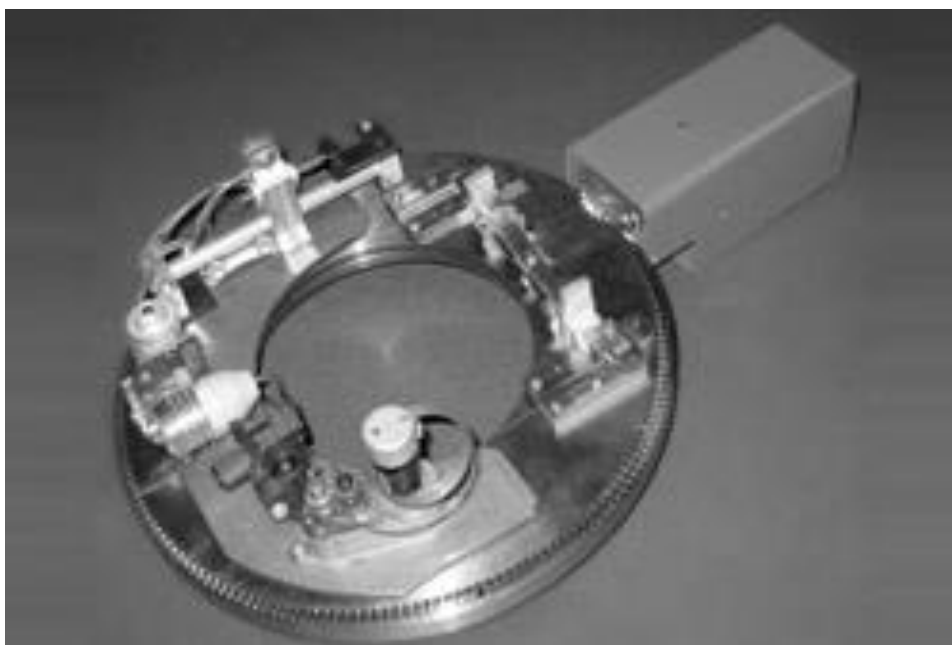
Фото сварочной головки ГНС-140
